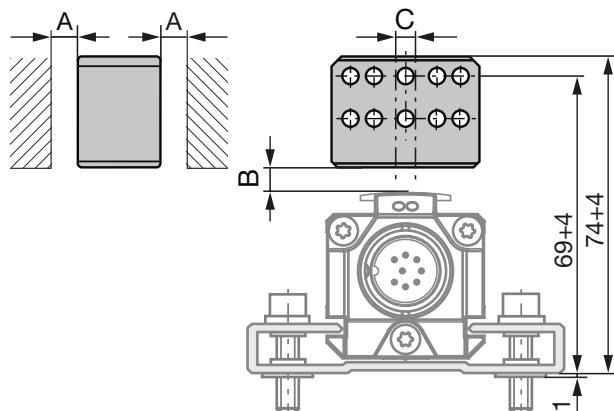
Dimensions et distances avec le capteur de position BTL6-A-3800-2
